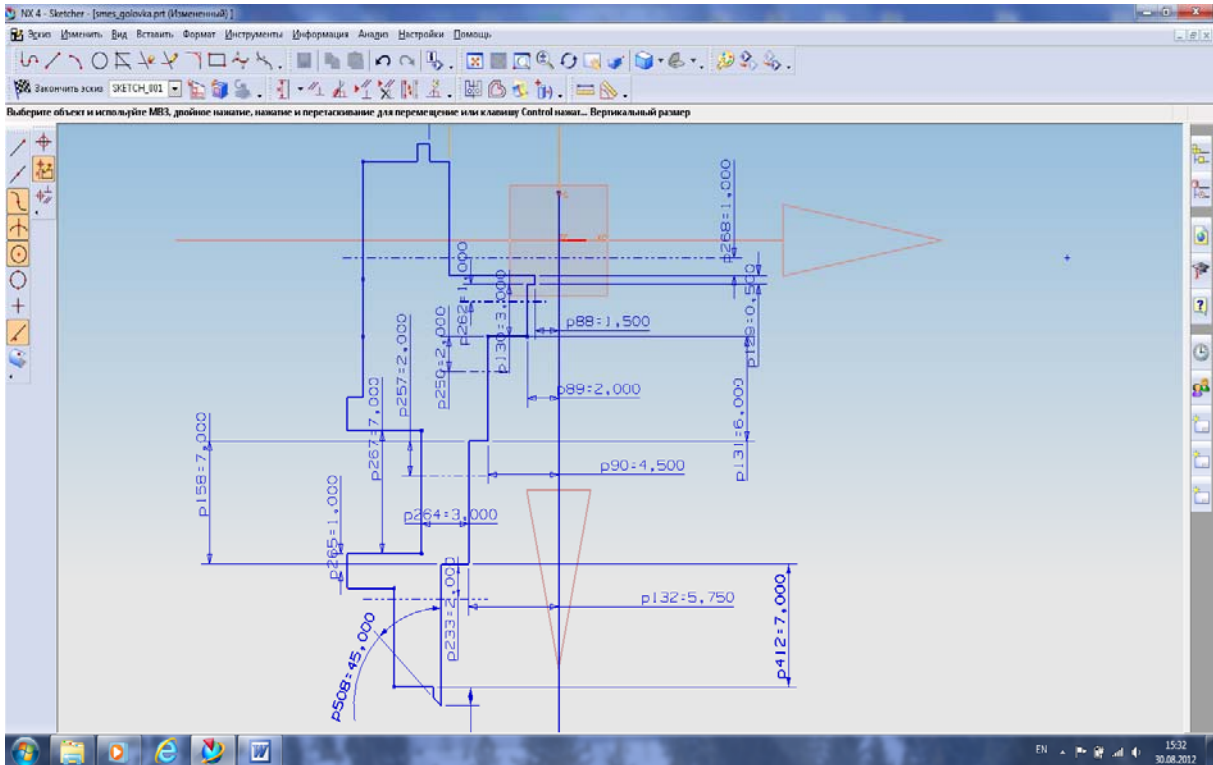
Плоскость эскизирования контуров смесительной головки двигателя
